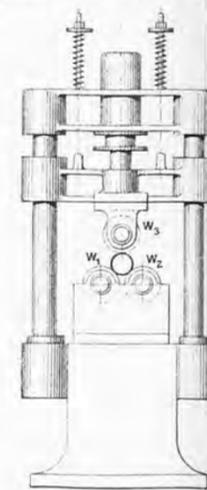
Walzwerk zur Herstellung geschweißter Hohlkörper.
